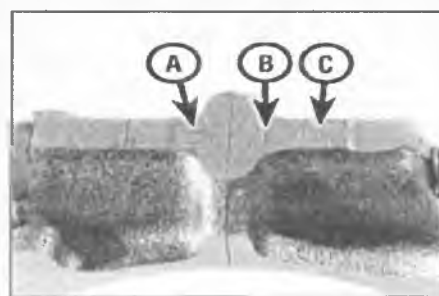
Маркировка шатуна/крышки подшипника – бензиновый двигатель
